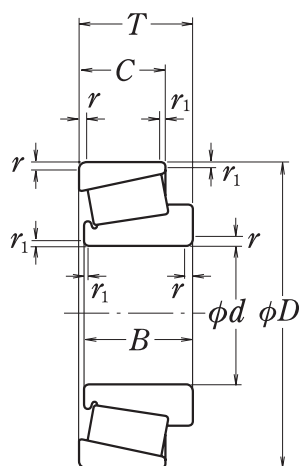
Dimensioni di ingombro dei cuscinetti a rulli conici
